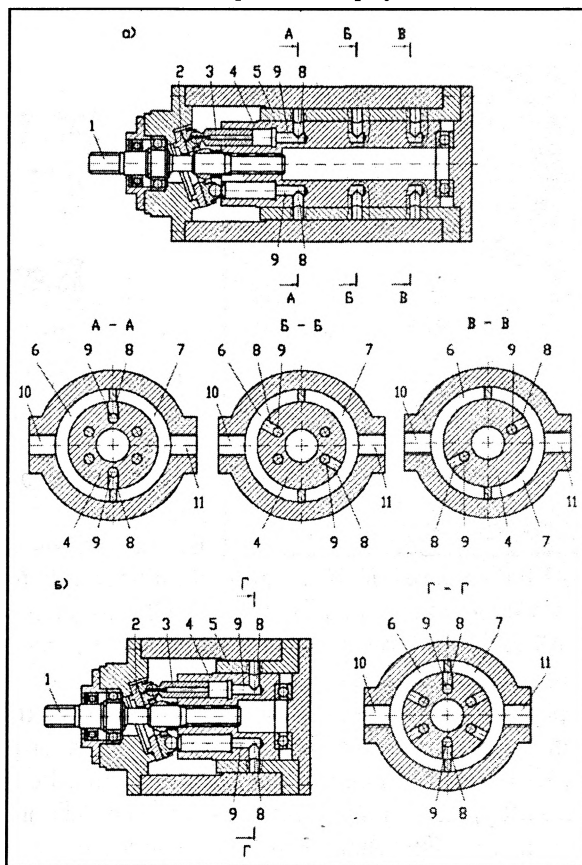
Аксиально-поршневая гидромашин с полукольцевыми пазами на образующей поверхности подшипника скольжения: 1 — ведущий вал; 2 — наклонная шайба; 3 — поршень; 4 — блок цилиндров; 5 — подшипник скольжения; 6, 1 — полукольцевые пазы; 8, 9 — каналы блока цилиндров; 10, 11 — каналы корпуса гидромашин
